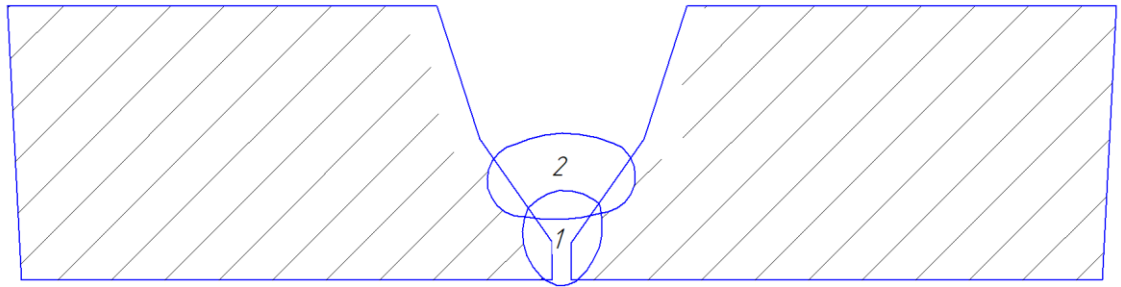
Сварка первого заполняющего слоя
